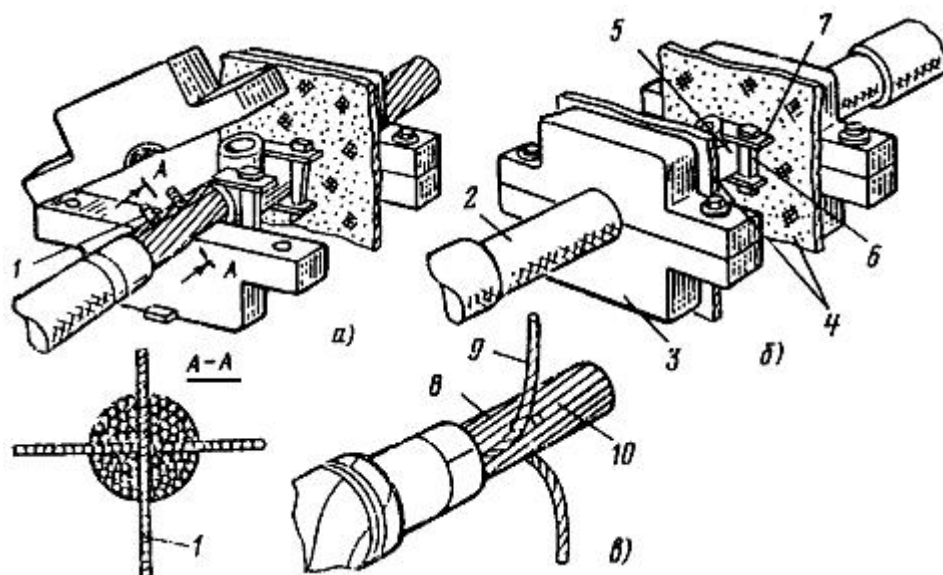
Подготовка к пропано-кислородной сварке кабелей АсВВ (а, б) и АСБ-2к (в)
